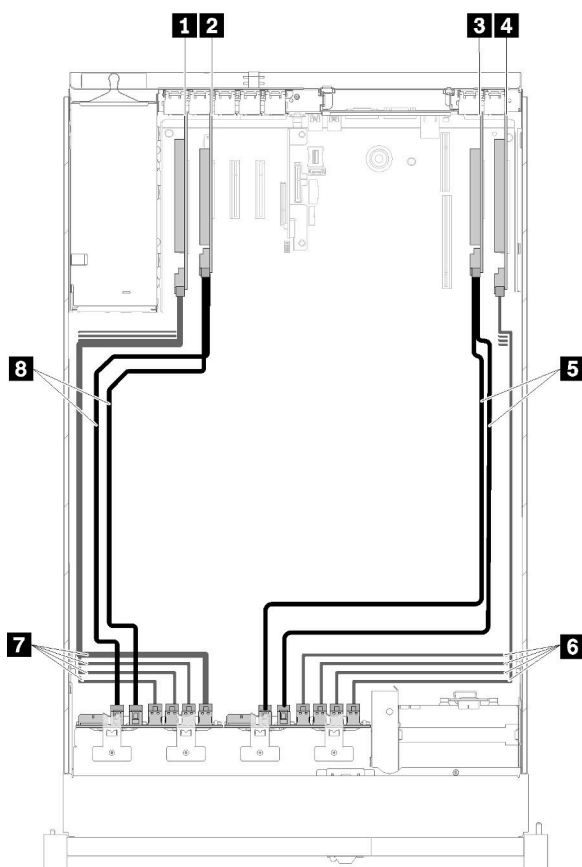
Disposición de los cables, Placa posterior de AnyBay + Placa posterior de AnyBay
